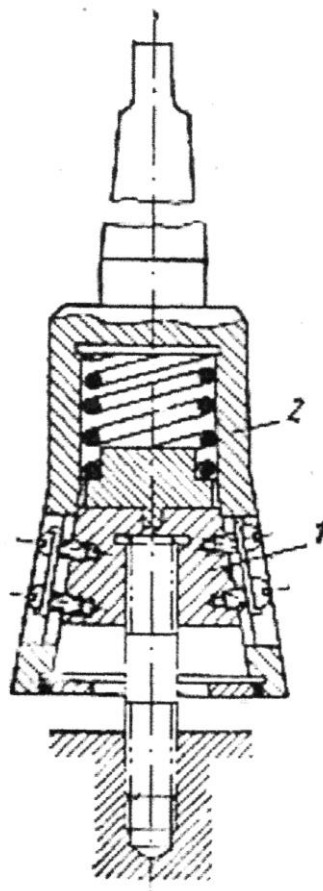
Самозатискний патрон для закручування шпильок
